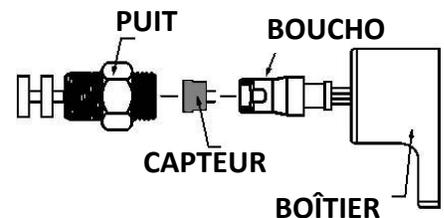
Vue éclatée du montage d'un thermostat de Classe I, Groupe D montrant le capteur de remplacement.
